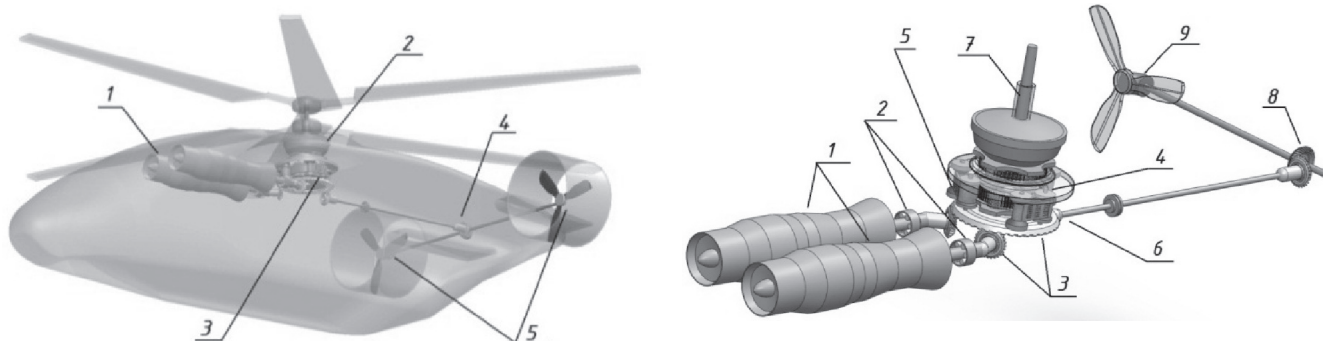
Модель компоновки бесступенчатой механической трансмиссии в составе скоростного вертолета: 1 — двигатели (ГТД); 2 — муфты свободного хода; 3 — коническая передача первой редукторной ступени; 4 — двухпоточный планетарный механизм бесступенчатой передачи; 5 — цепные вариаторы; 6 — привод толкающих винтов (коническая передача); 7 — планетарная часть главного редуктора с валами несущих винтов; 8 — угловой привод (промежуточный редуктор); 9 — угловые редукторы привода толкающих винтов
